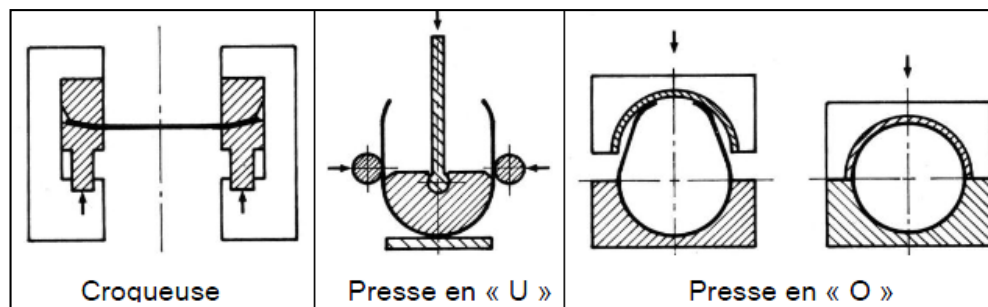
Formage en U, formage en O, et soudage de la fabrication des tubes soudés en long [4].
